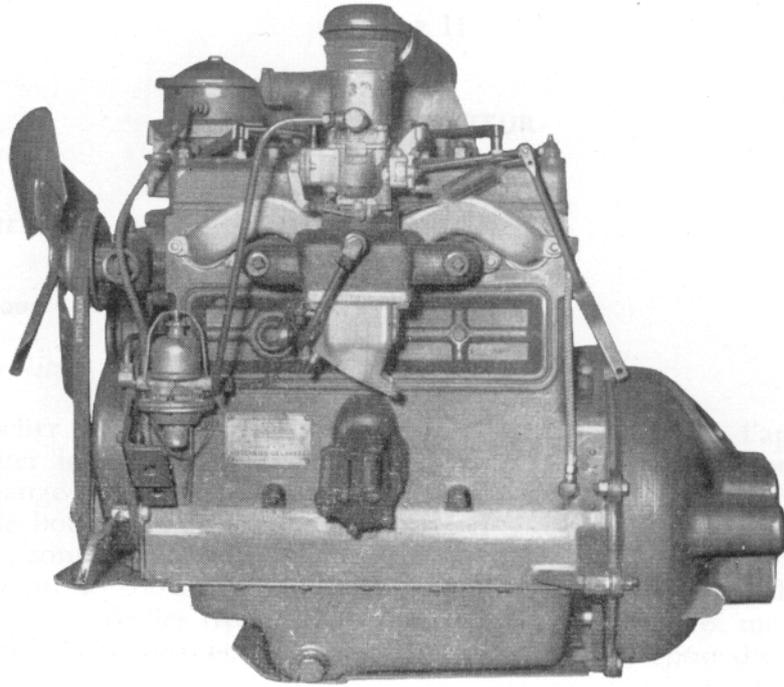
Vue du côté gauche du moteur assemblé.
